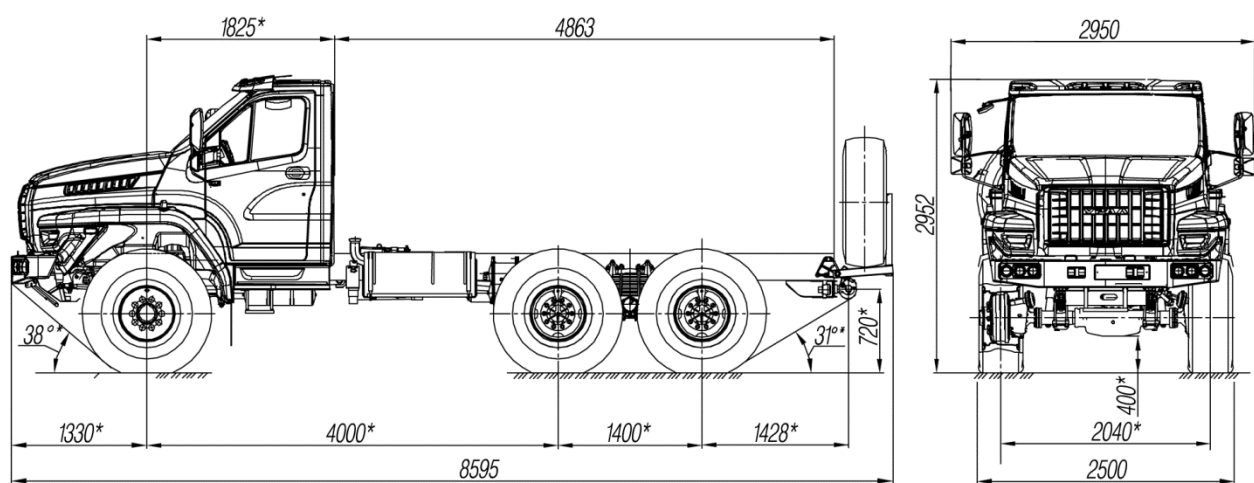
Габаритные размеры шасси Урал-43203-6151-73
